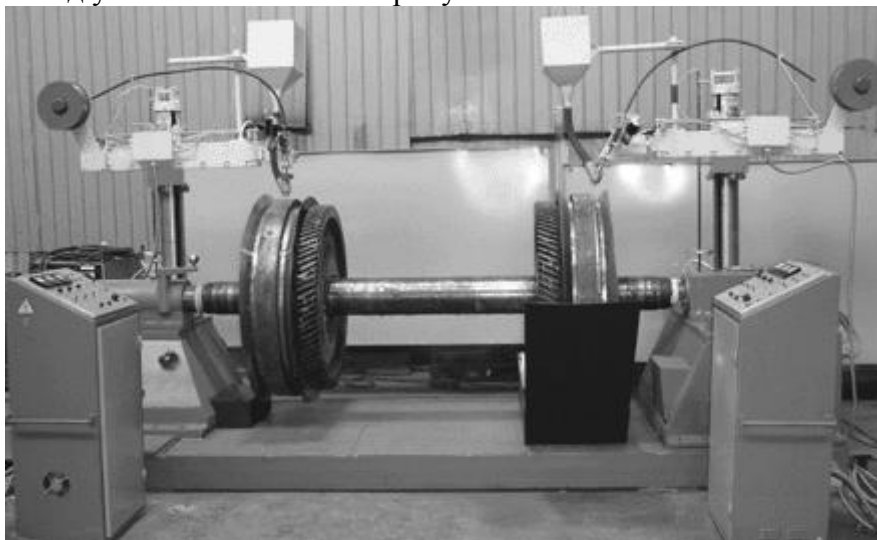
Установка для автоматической наплавки под слоем флюса гребней бандажей после выкатки колесной пары из-под электровоза
